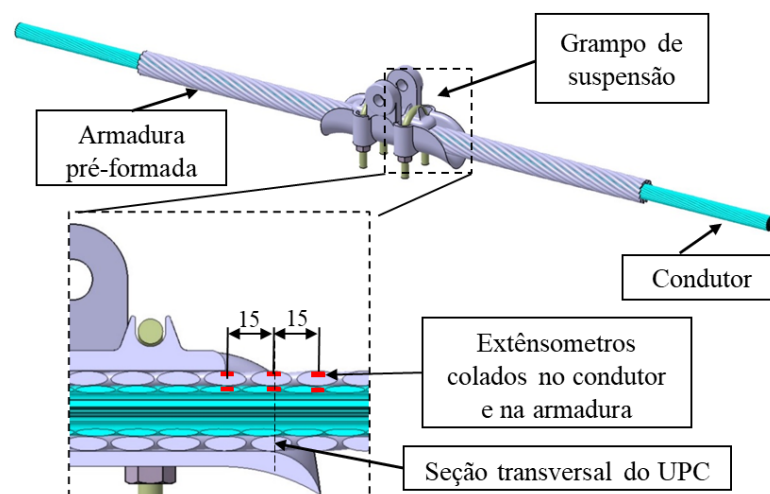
Posição dos extensômetros montados no grampo de suspensão metálico com armadura.
